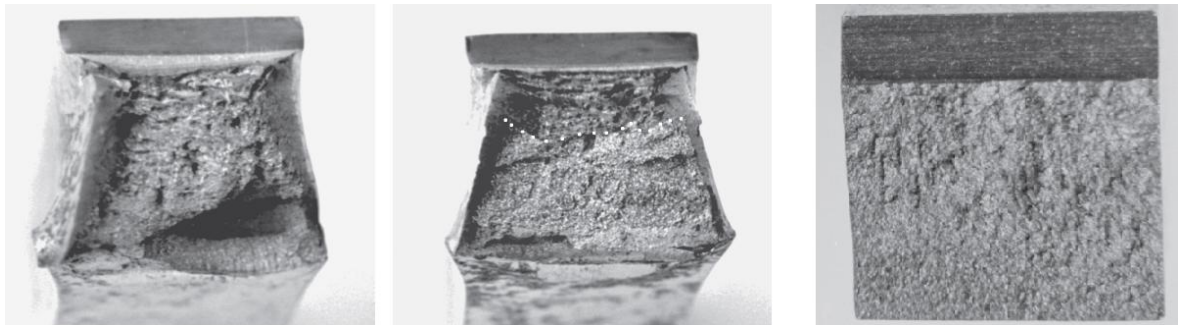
Faciès de rupture sur de l'acier 36MND5.
